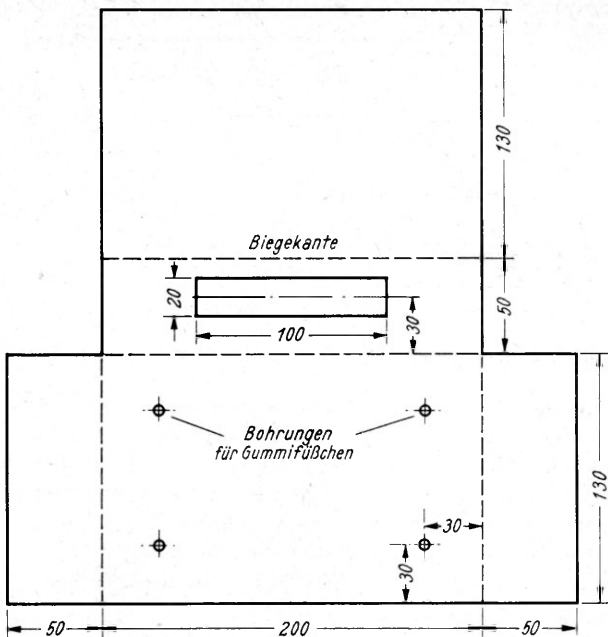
Abmessungen der Metallplatte für die Gehäusehaube
